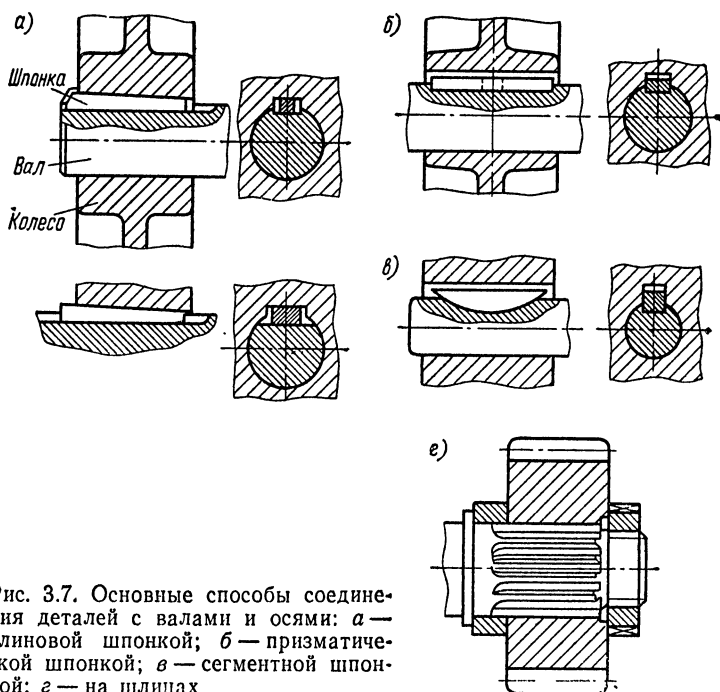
Основные способы соединения деталей с валами и осями: *а* — клиновой шпонкой; *б* — призматической шпонкой; *в* — сегментной шпонкой; *г* — на шлицах
